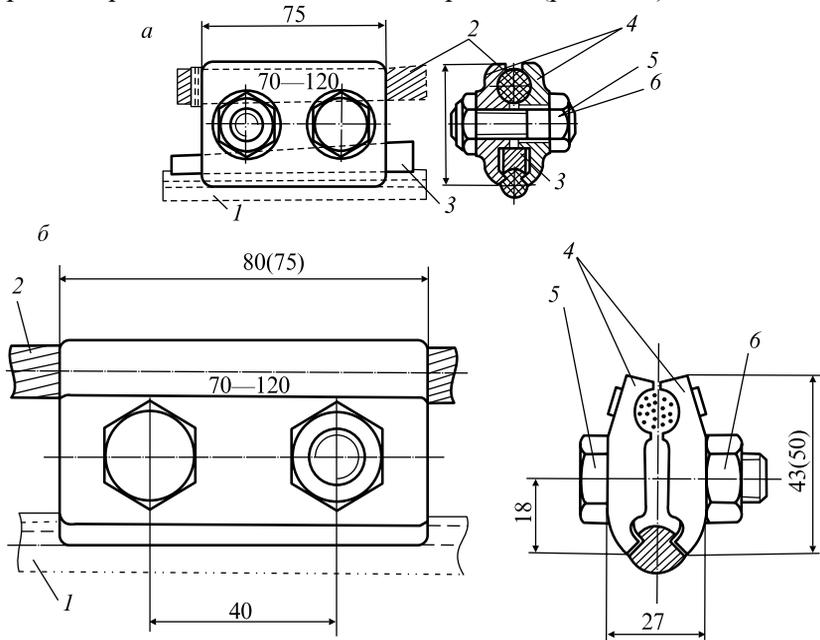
Питающие зажимы: *a* — с клином; *б* — с насечкой без клина; 1 — контактный провод; 2 — соединительный провод; 3 — клин; 4 — плашка; 5 — болт; 6 — гайка
